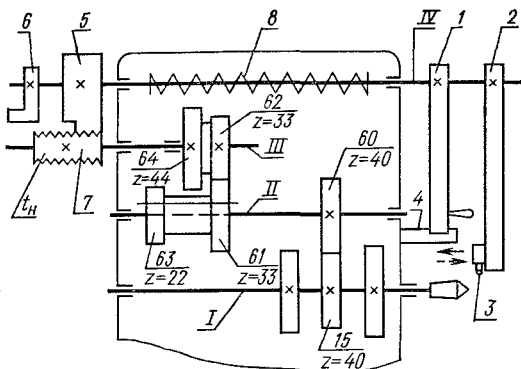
Кинематическая схема токарно-револьверного станка мод. 1А341
